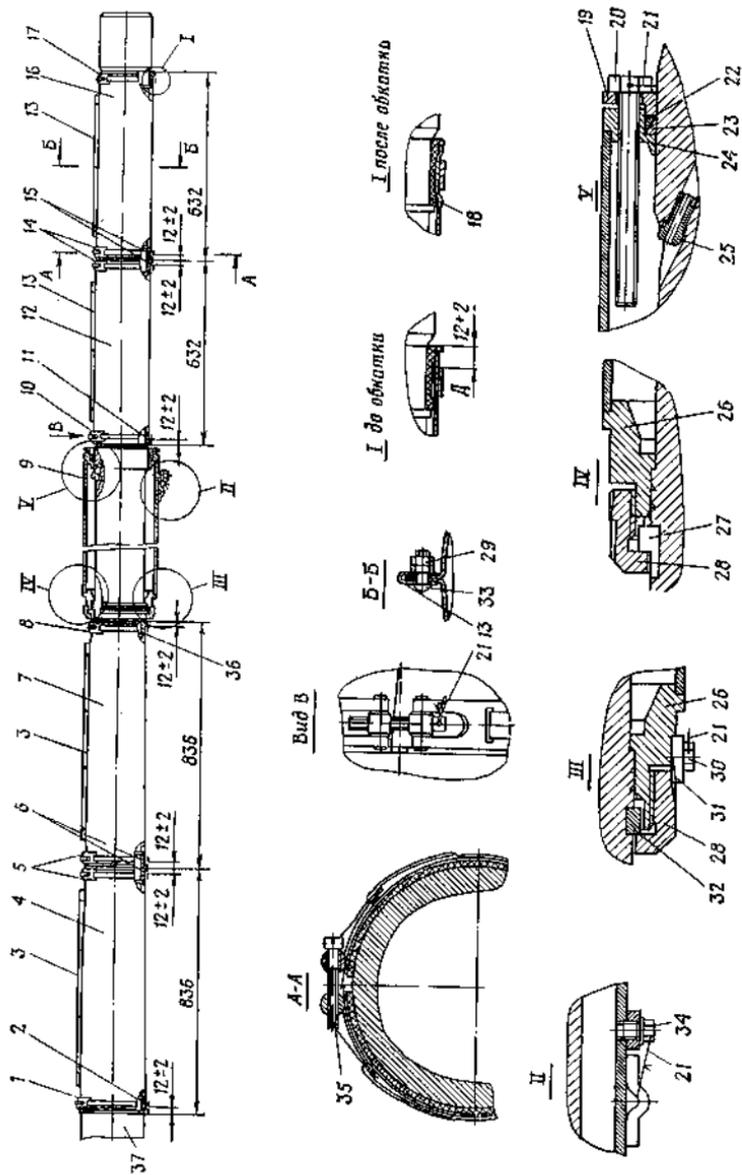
Ствол с термозащитным кожухом и ресивером:
